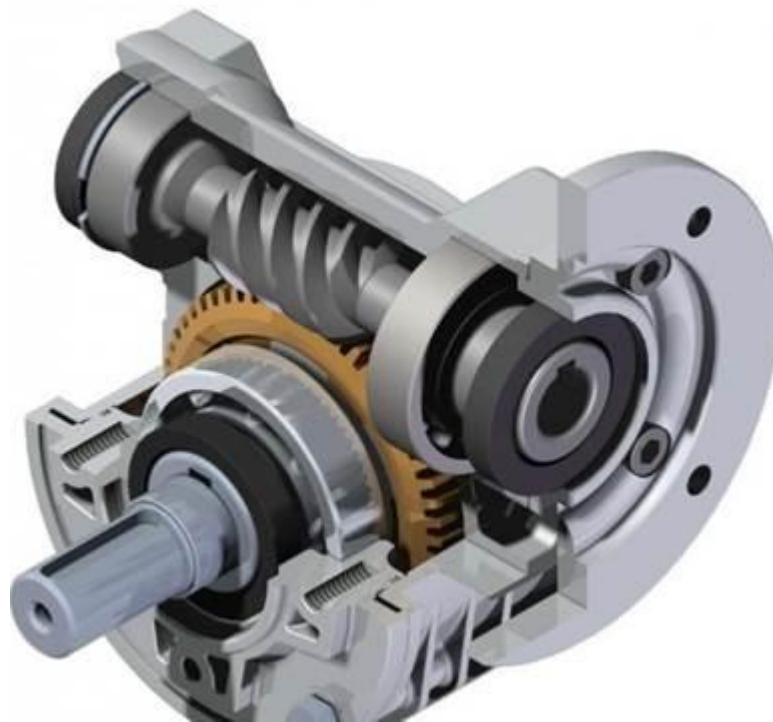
Схеми передавачів за конструкцією корпусу
